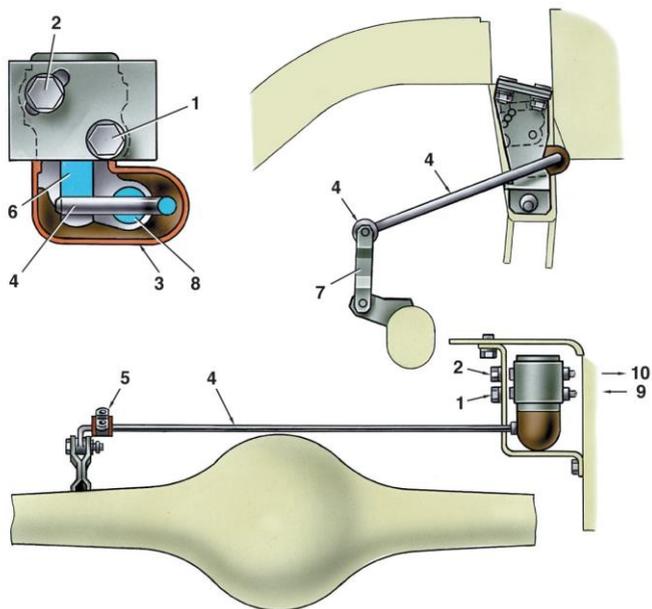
Схема установки регулятора давления задних тормозов и его регулировки [49]:
